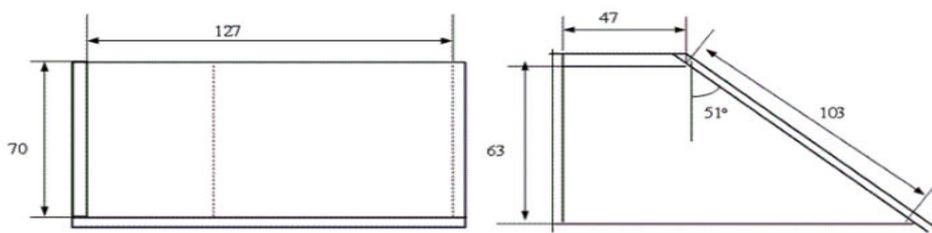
Схема угловой ячейки Хуллы. Вид сбоку и вид сверху
